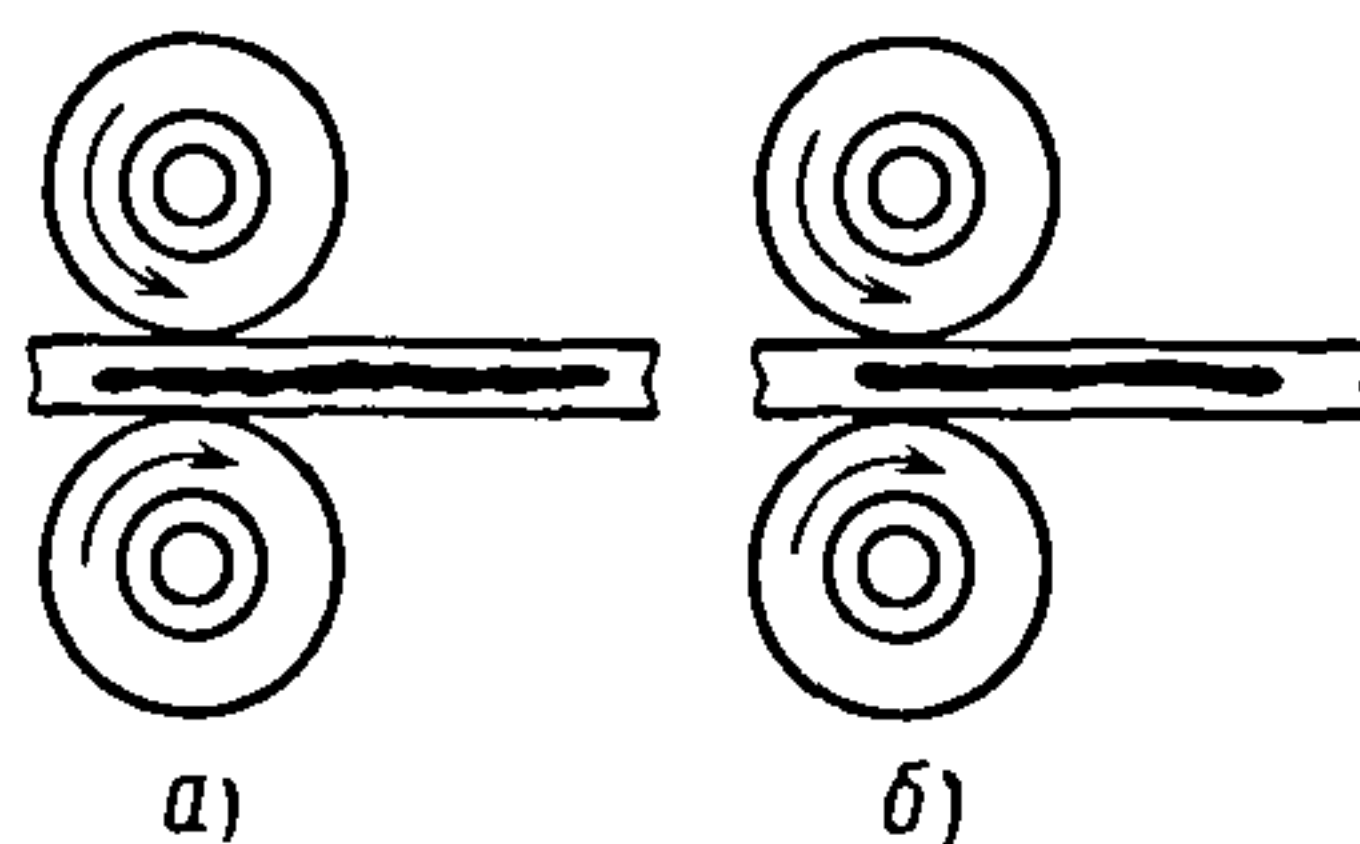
Схемы шовной контактной сварки в импульсном (а) и непрерывном (б) режимах
